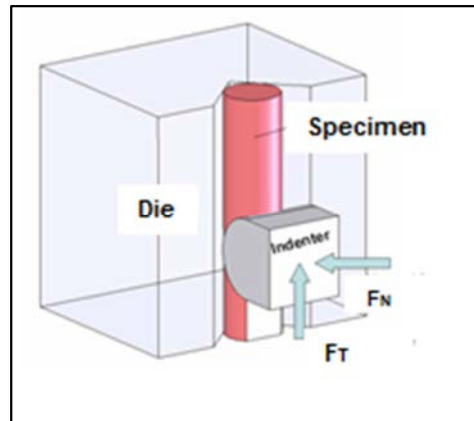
Schematizzazione dell'*upsetting-sliding test
